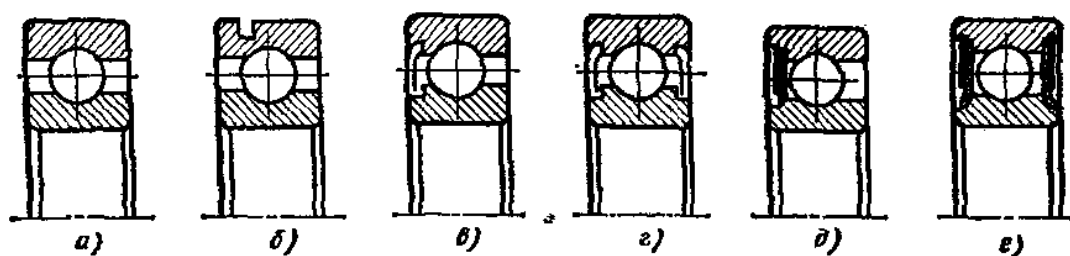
Шарикоподшипники радиальные однорядные типов:
